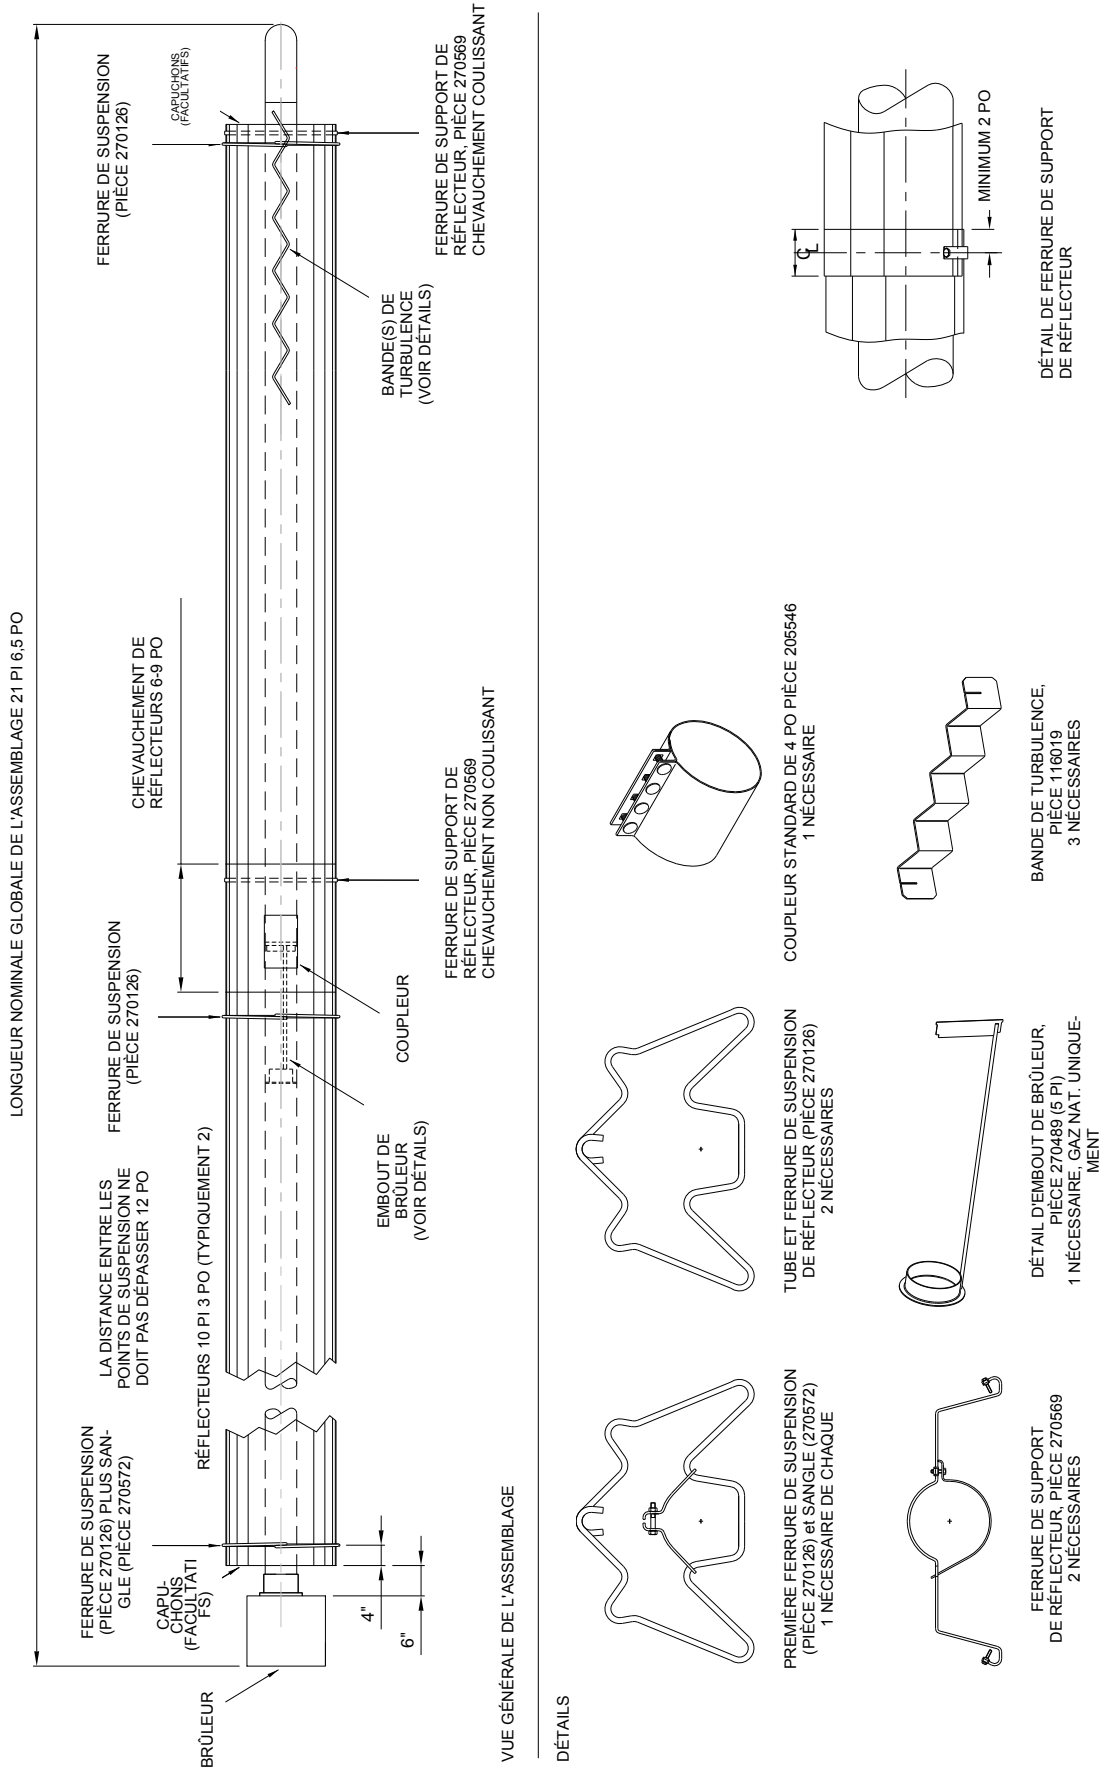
Assemblage de radiateur : Modèle linéaire 60-S30, 80-S30, 100-S30 et 125-S30
